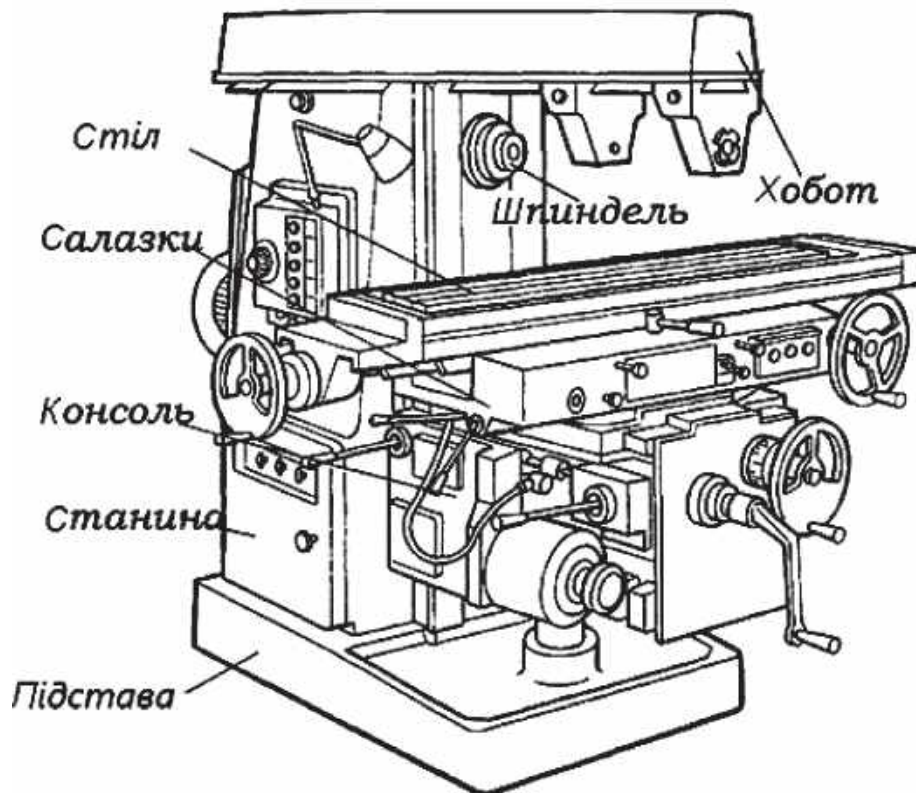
Консольний горизонтально-фрезерний верстат
